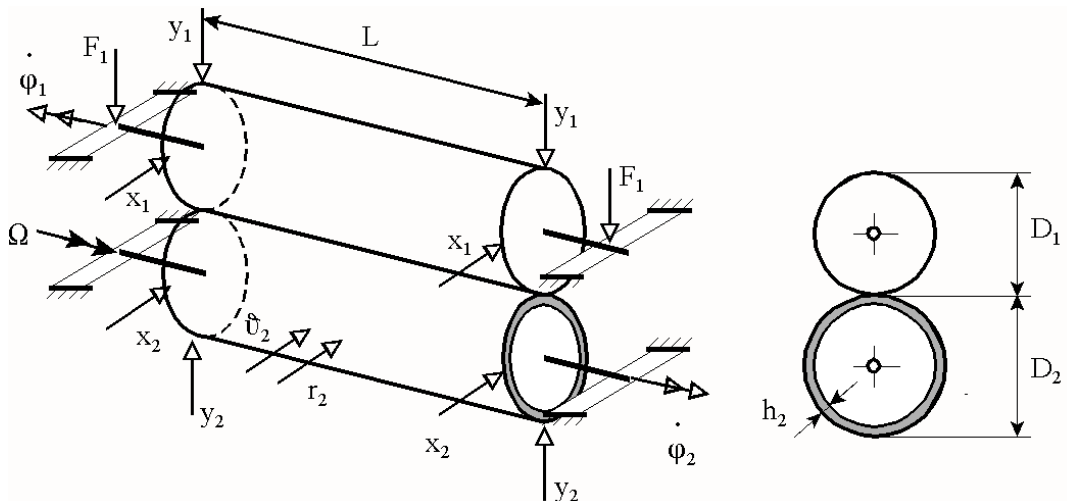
Schema des Versuchsstands im Versuchsfeld des Fraunhofer Instituts Werkzeugmaschinen und Umformtechnik in Chemnitz
